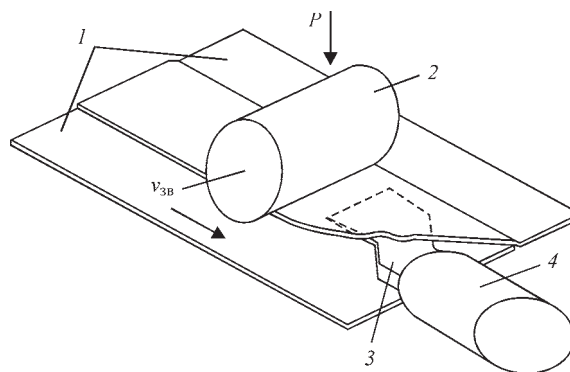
Схема напускового зварювання тканин з ПВХ покриттям за допомогою гарячого повітря: 1 – тканини, що зварюються; 2 – притискний ролик; 3 – сопло для напускового зварювання; 4 – нагрівальний апарат гарячого повітря
